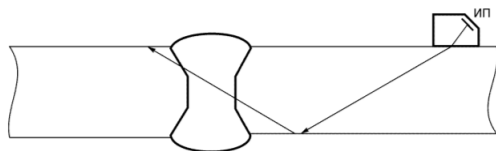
Схема прозвучивания стыкового сварного соединения однократно отраженным лучом
